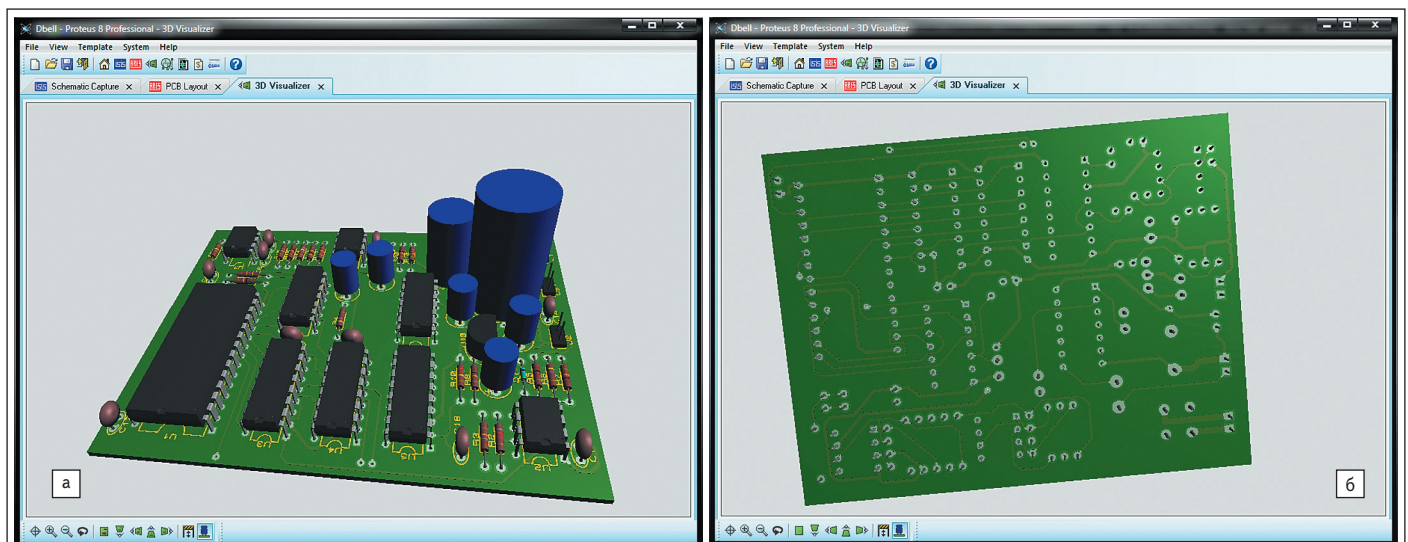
3D-изображение печатной платы на вкладке 3D Visualizer: а) вид сверху; б) вид снизу
